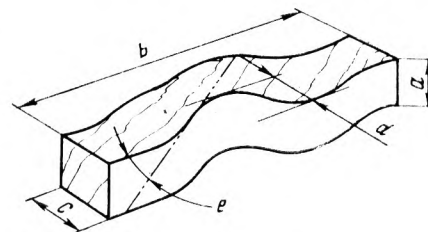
Схема выпилки детали на станке CBS Electro-48:
